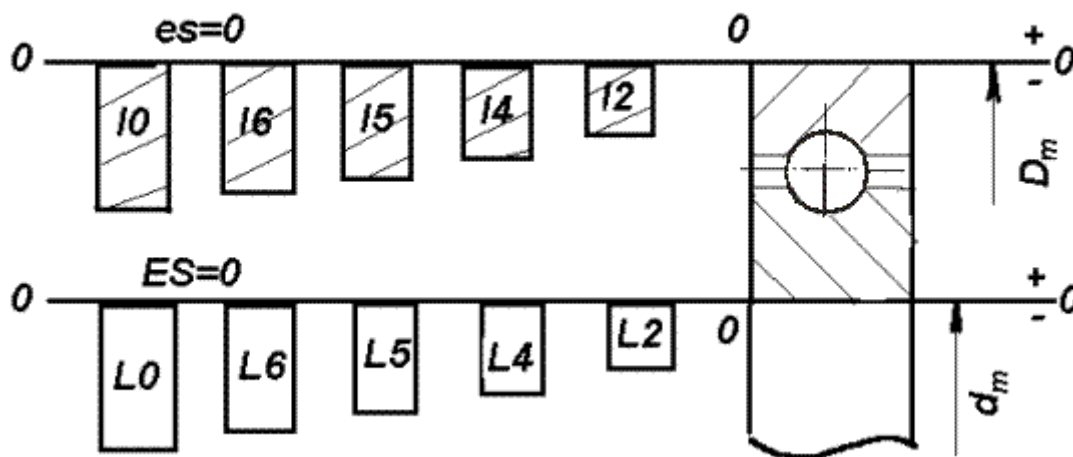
Схема расположения полей допусков на наружный и внутренний диаметры подшипников качения.
